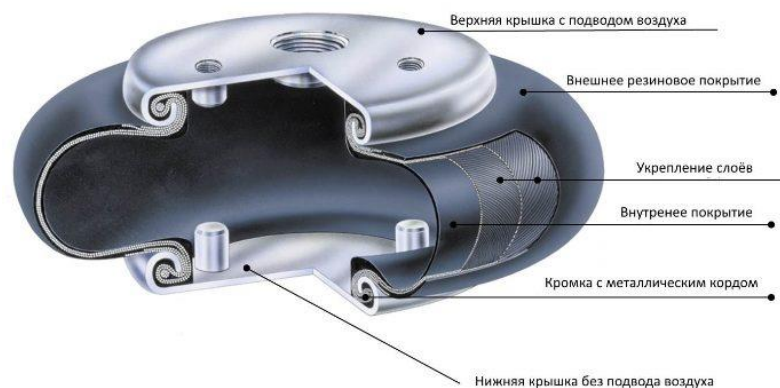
Сильфонный пневмоцилиндр
